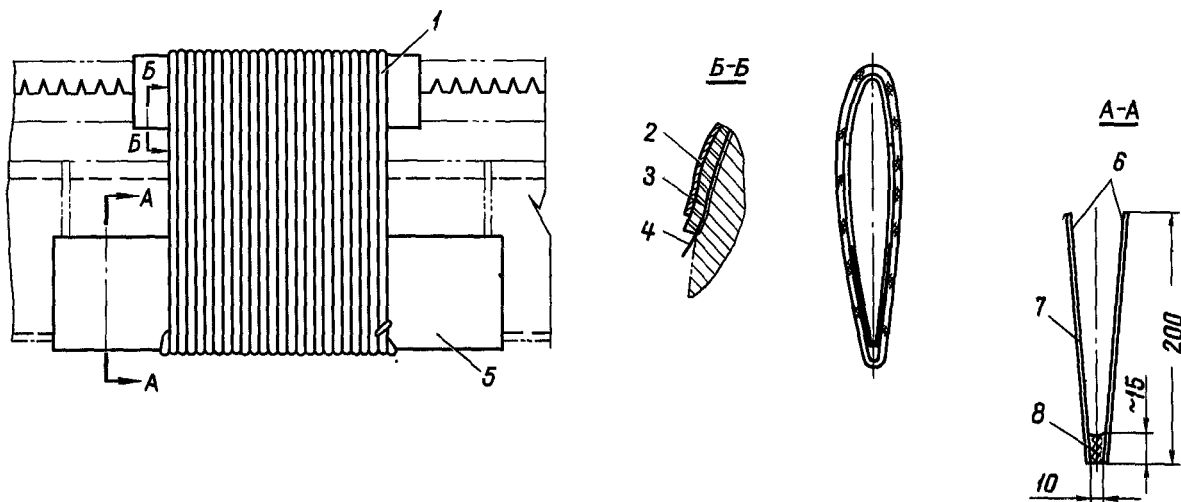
Схема приклейки оковки и противобрызгивной наклейки:
